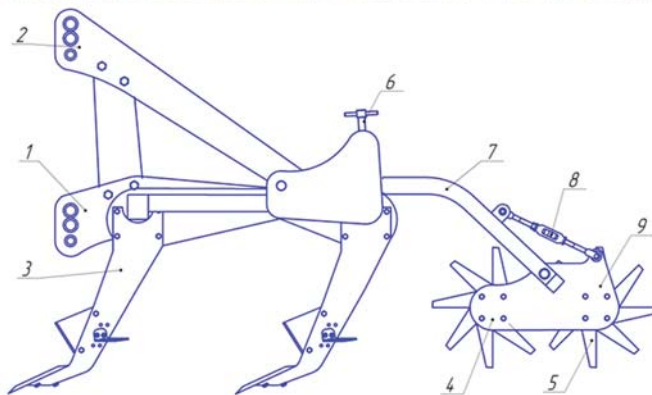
Комбінований чизельний розпушувач шириною захвату 3 м: 1 – рама; 2 – верхня ланка націпного пристрою; 3 – чизельний робочий орган; 4 – коток передній; 5 – коток задній; 6 – гвинтовий механізм регулювання глибини обробітки ґрунту; 7 – кронштейн кріплення котків; 8 – гвинтова тяга регулювання положення котків; 9 – бокова пластина кріплення котків
